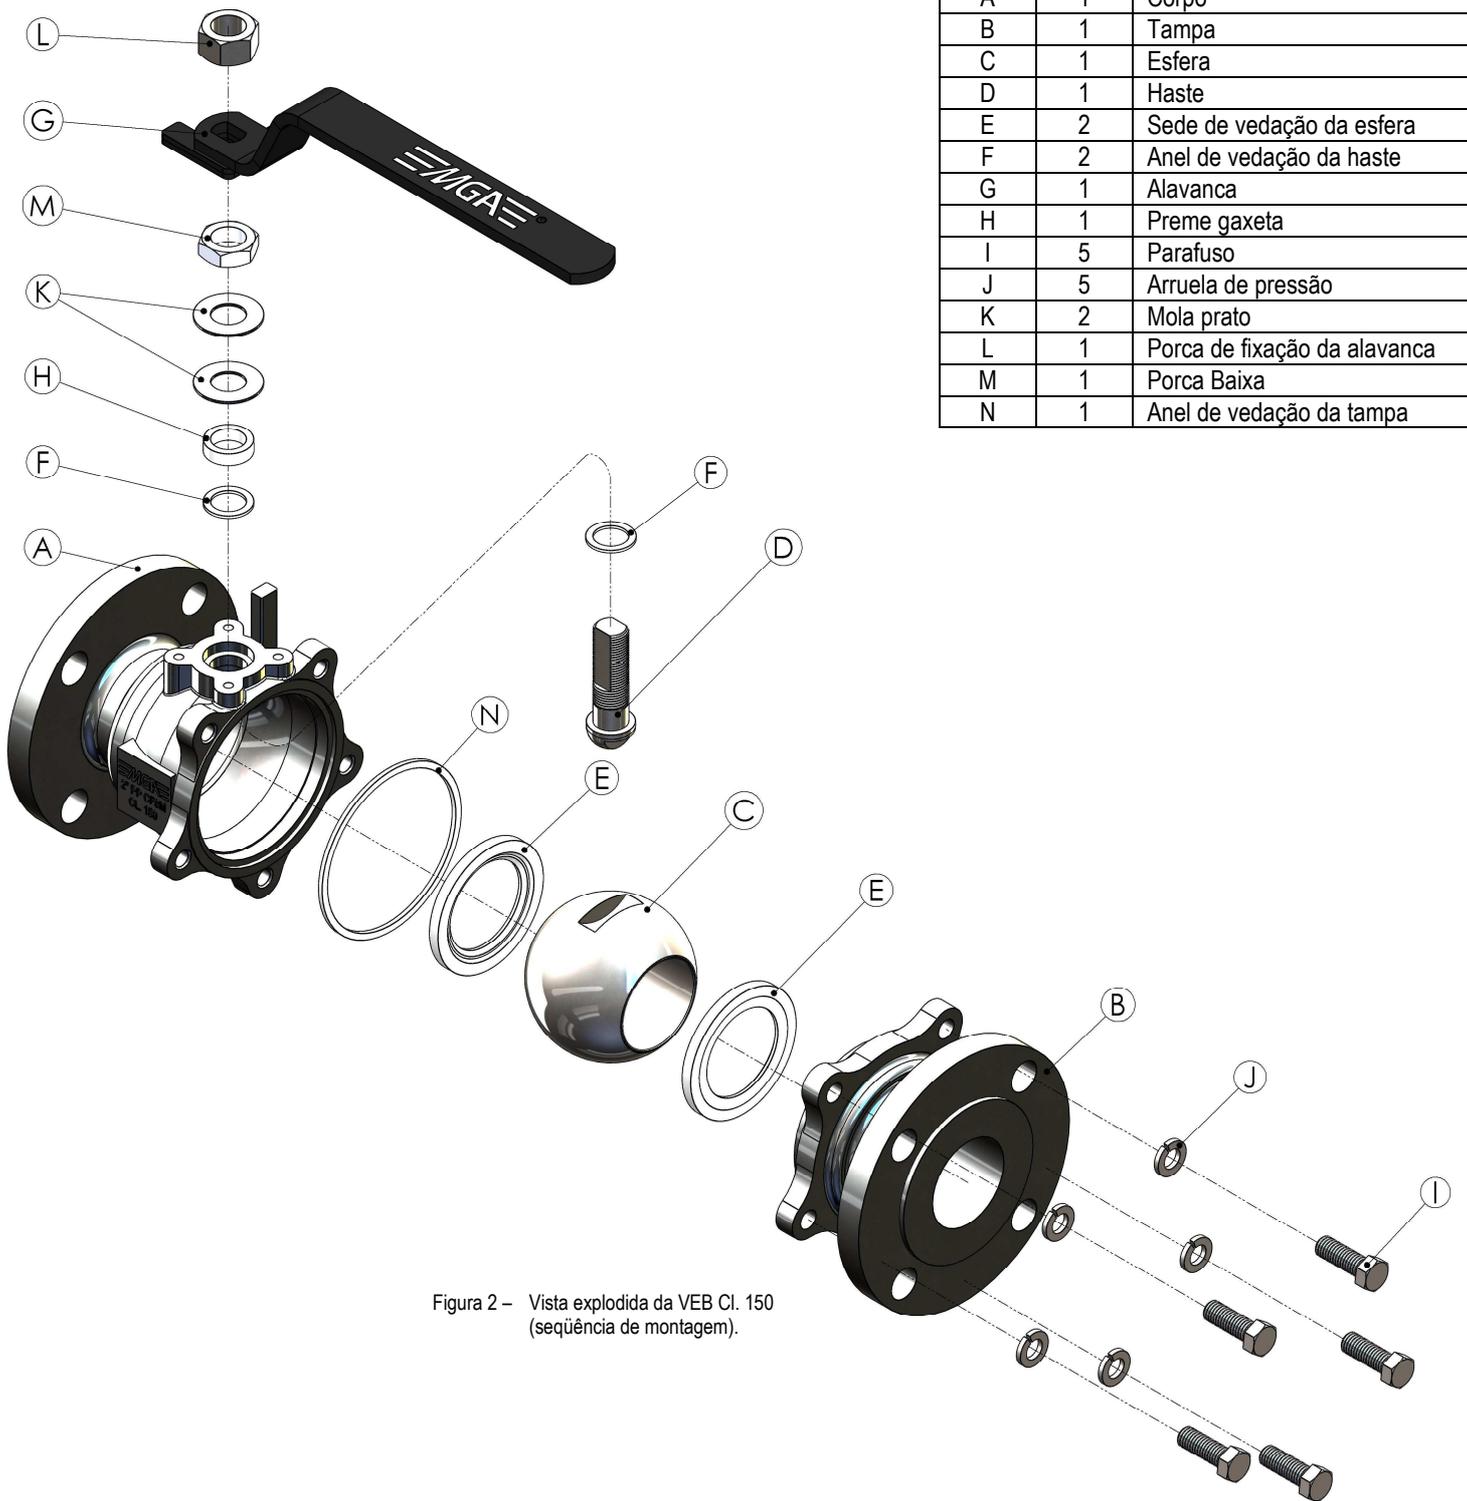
Vista explodida da VEB Cl. 150 (seqüência de montagem).
